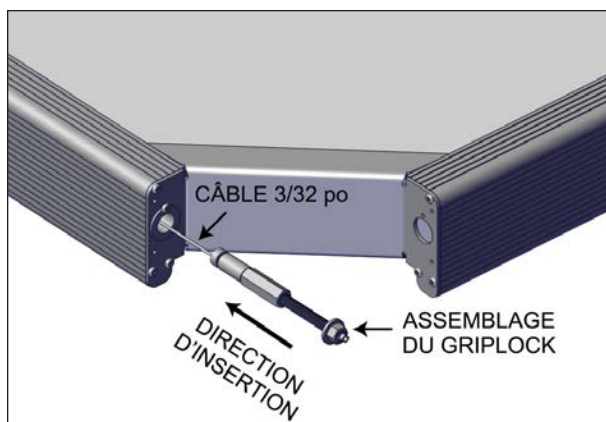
ASSEMBLAGE DU GRIPLOCK
